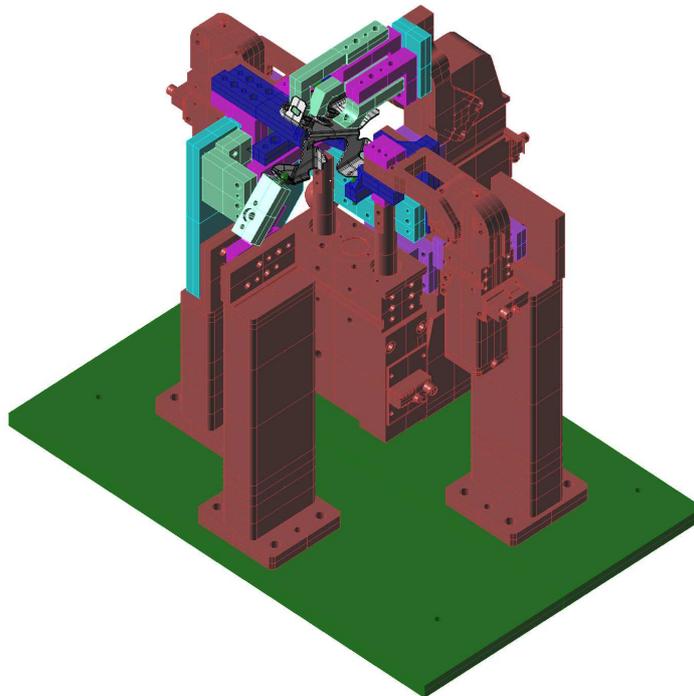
Attrezzatura di geometria OP.10 SX
